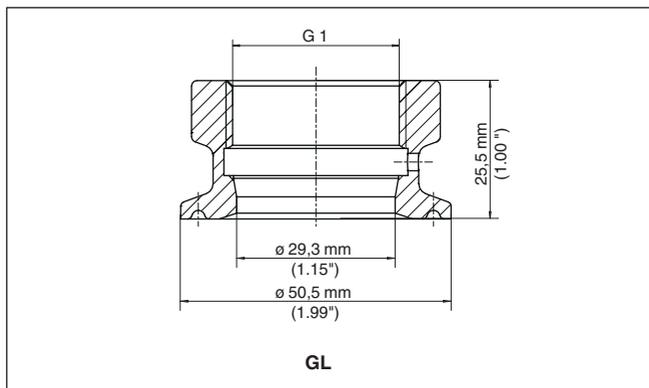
Dimensiones adaptador de rosca G1 (DIN 3852-X) a Clamp 1½" (DIN 32676, ISO 2852) PN 16
